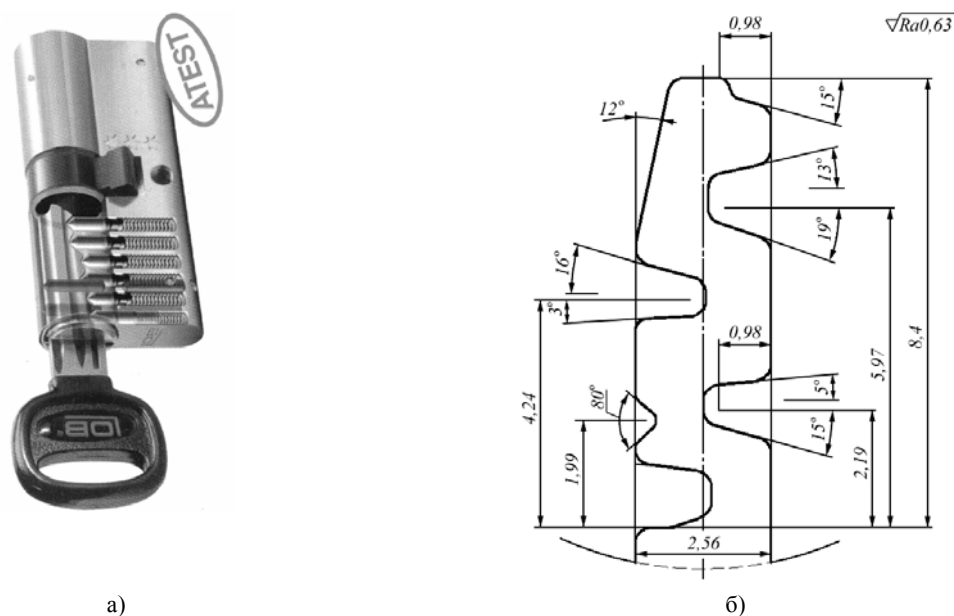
Принцип работы замка и типовой профиль паза вкладыша (приведены номинальные размеры)
